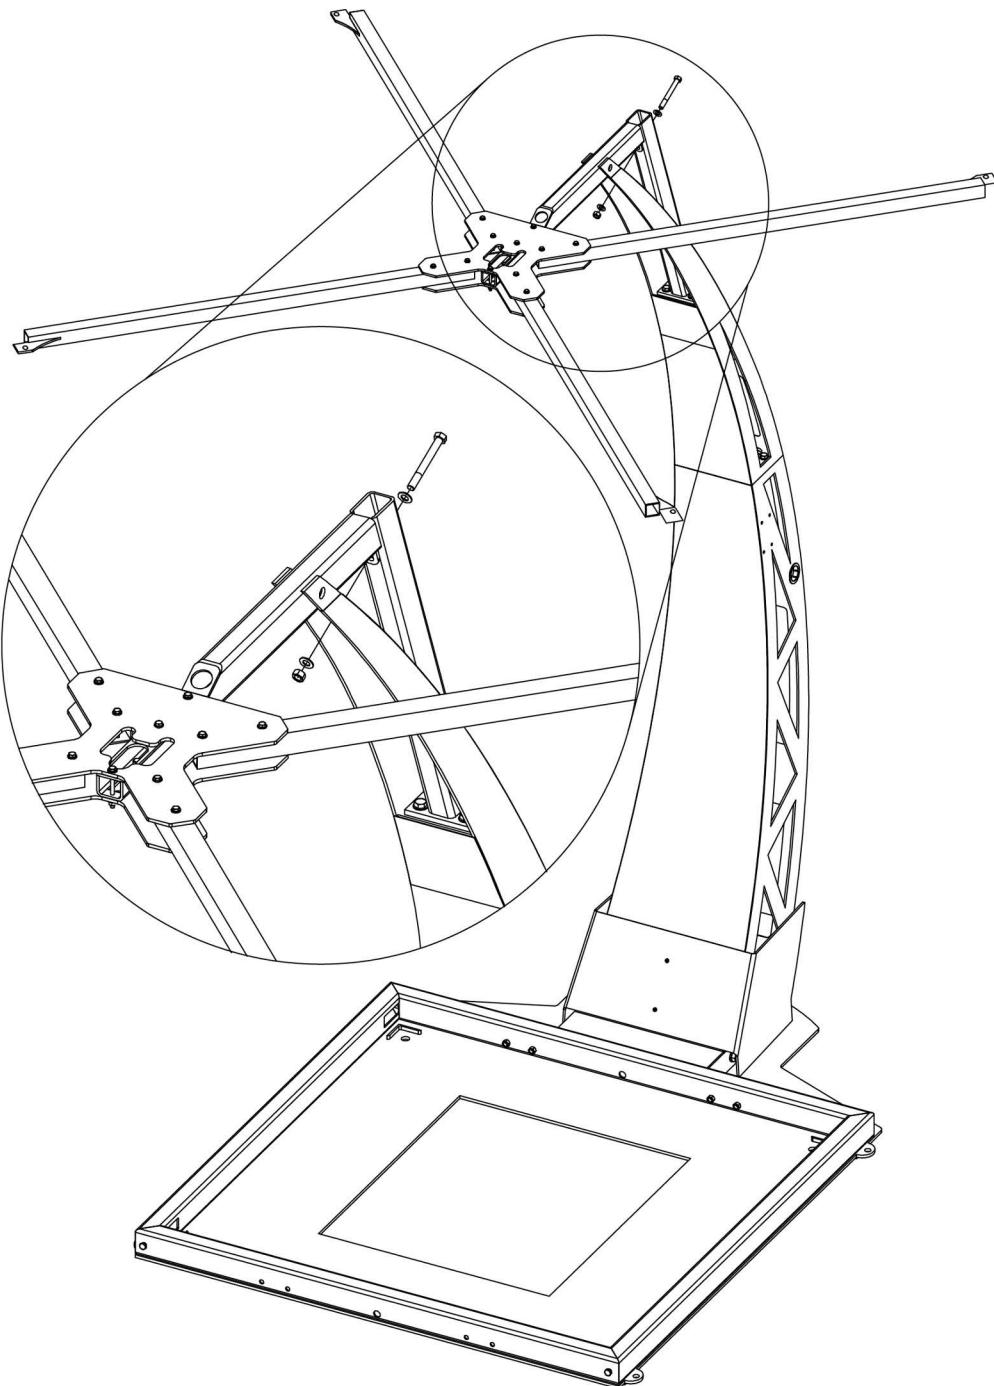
Ausrichtungsschraube der Montagespinne
